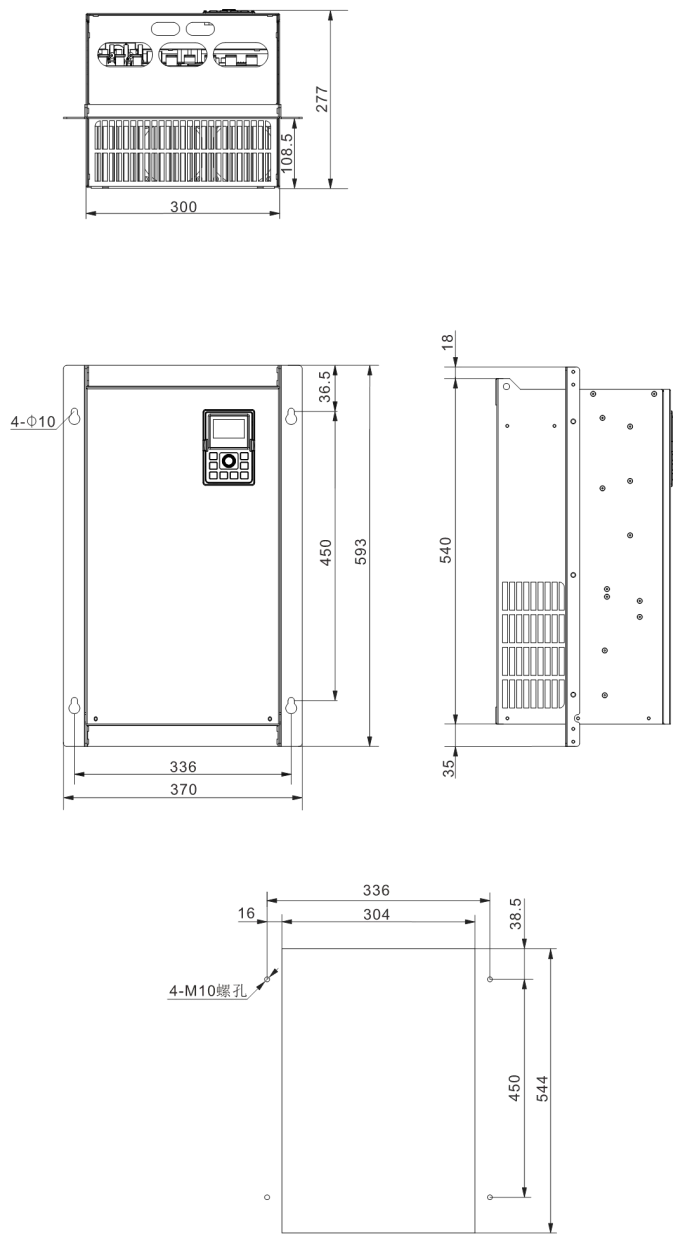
SIZE G(45-55kw)机型开孔尺寸
